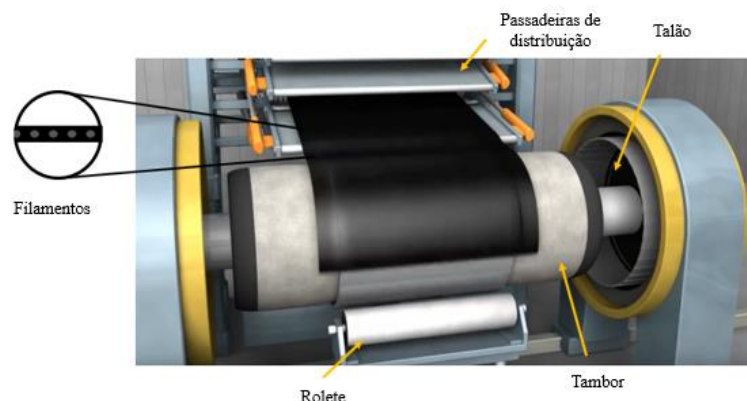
Representação da colocação das telas no tambor da máquina de construção (U.S. Tire Manufacturers Association, 2018).
